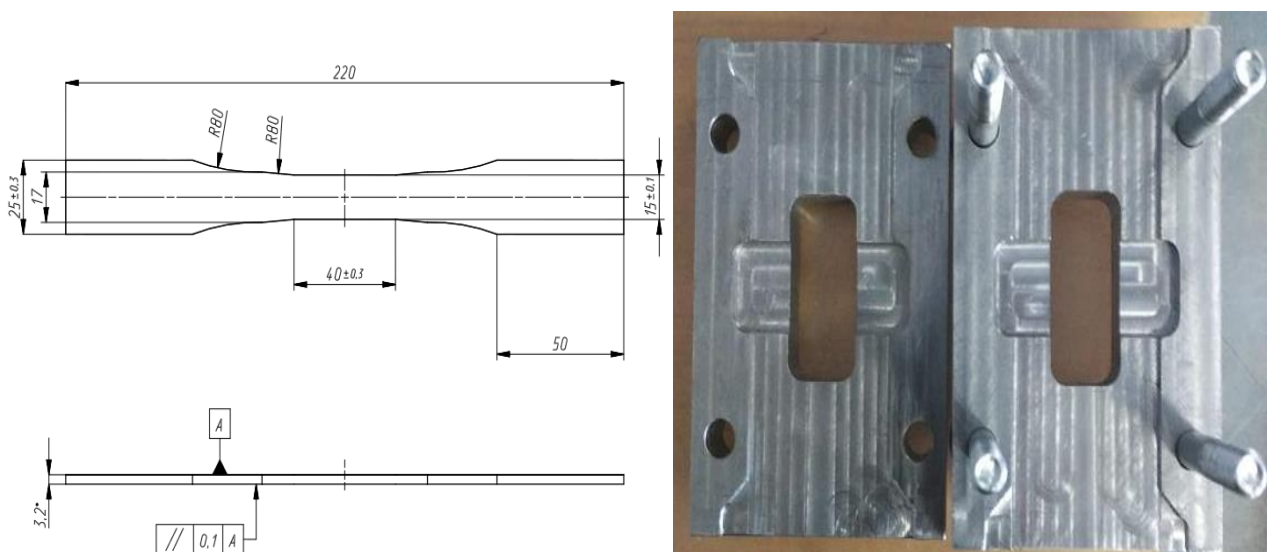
Чертеж образца и противоизгибное приспособление для методики ФГУП «ЦАГИ»
